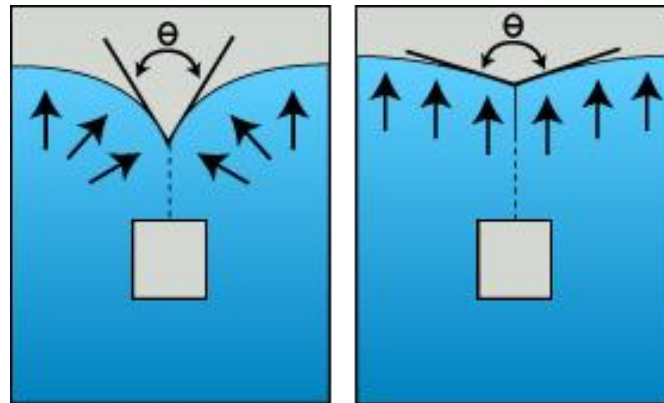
Línea de soldadura (izquierda) y línea de flujo (derecha)
